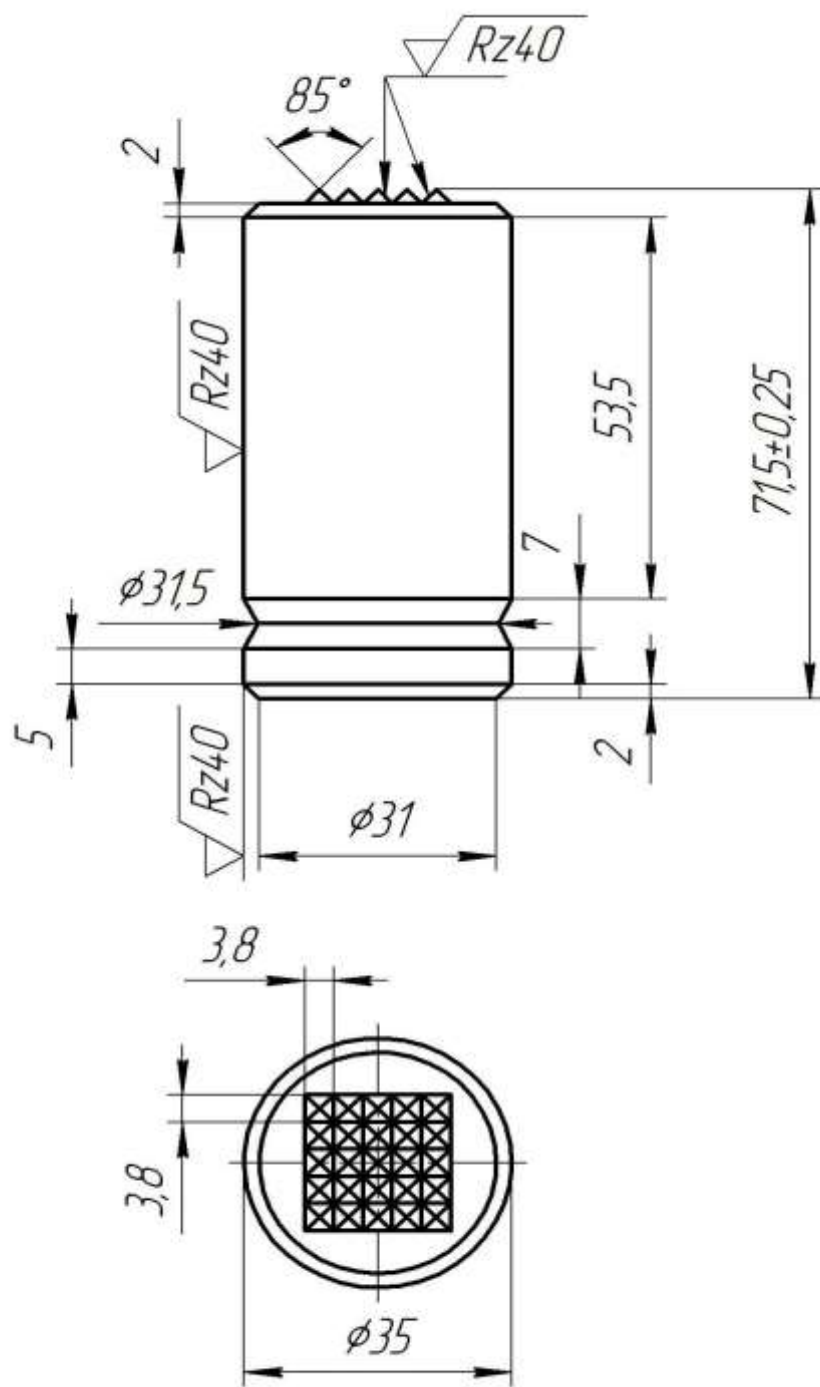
Затискний пристрій шиномонтажного верстата (базовий варіант)
